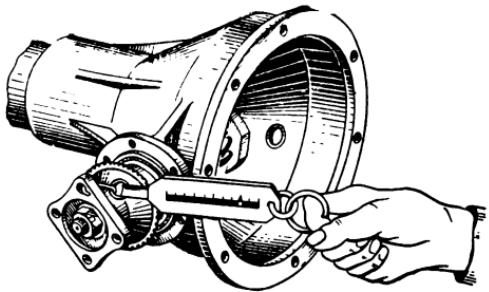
Проверка затяжки подшипников ведущей шестерни
